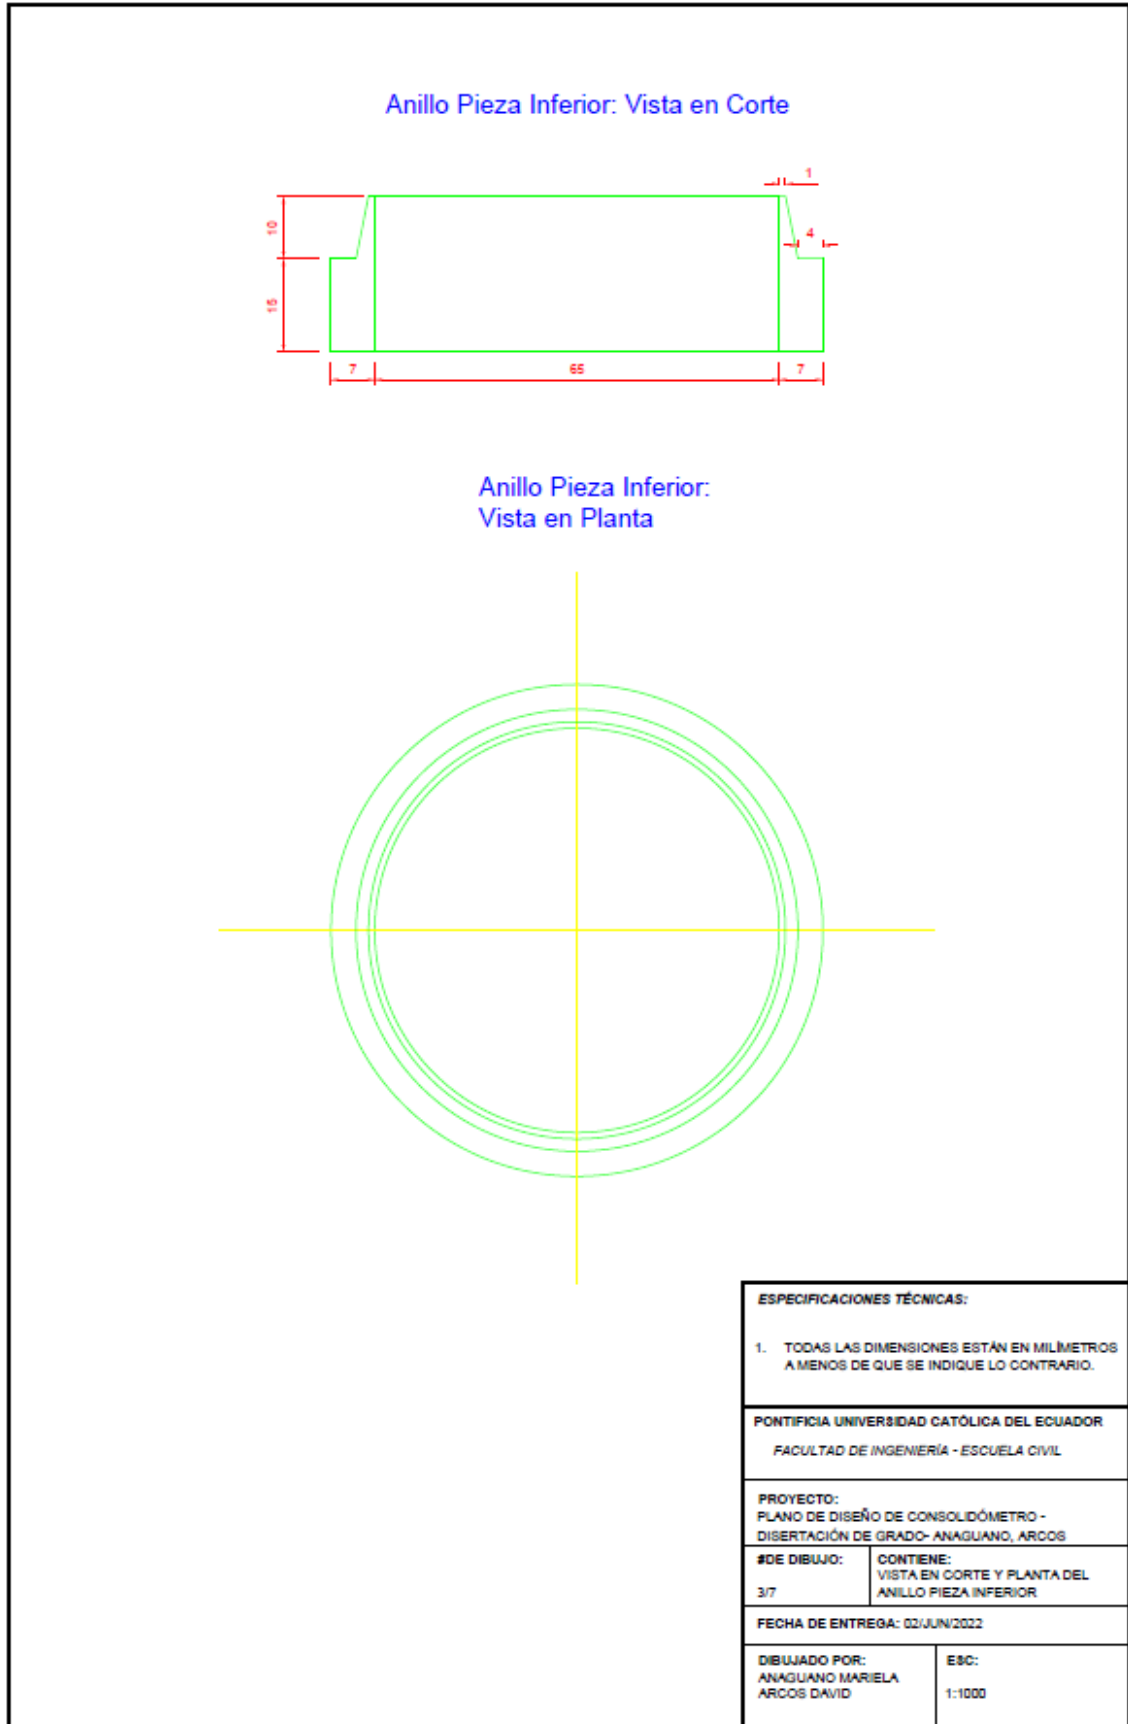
Plano de diseño del consolidómetro. Vista en corte y planta del anillo pieza inferior. Elaboración propia
